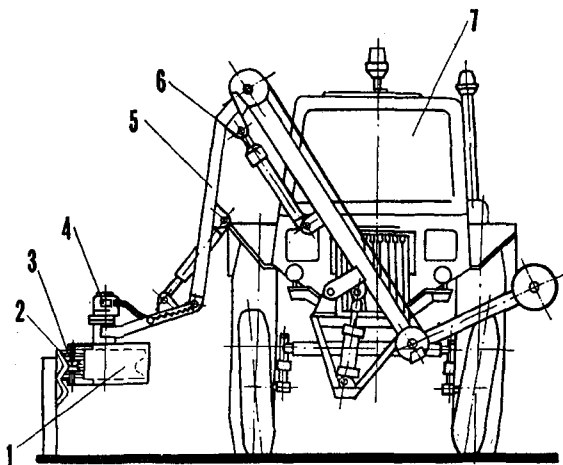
Машина для очистки криволинейного бруса: 1 – кожух рабочего органа; 2 – щетка; 3 – направляющий ролик; 4 – гидромотор привода рабочего органа; 5 – механизм навески; 6 – система гидропривода; 7 – базовое шасси.
